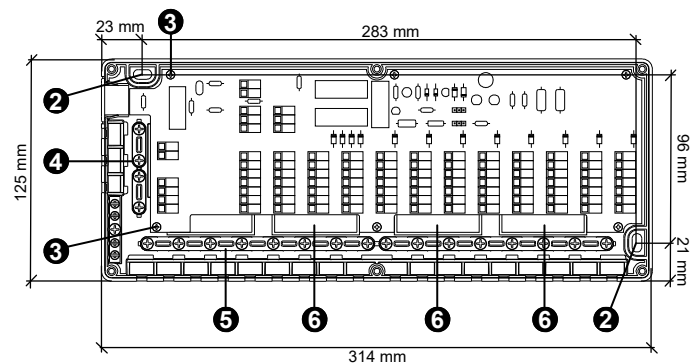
Vista interna e parti meccaniche / Internal view and parts / Vue interne et parties mécaniques / Vista interna y partes mecánicas.
